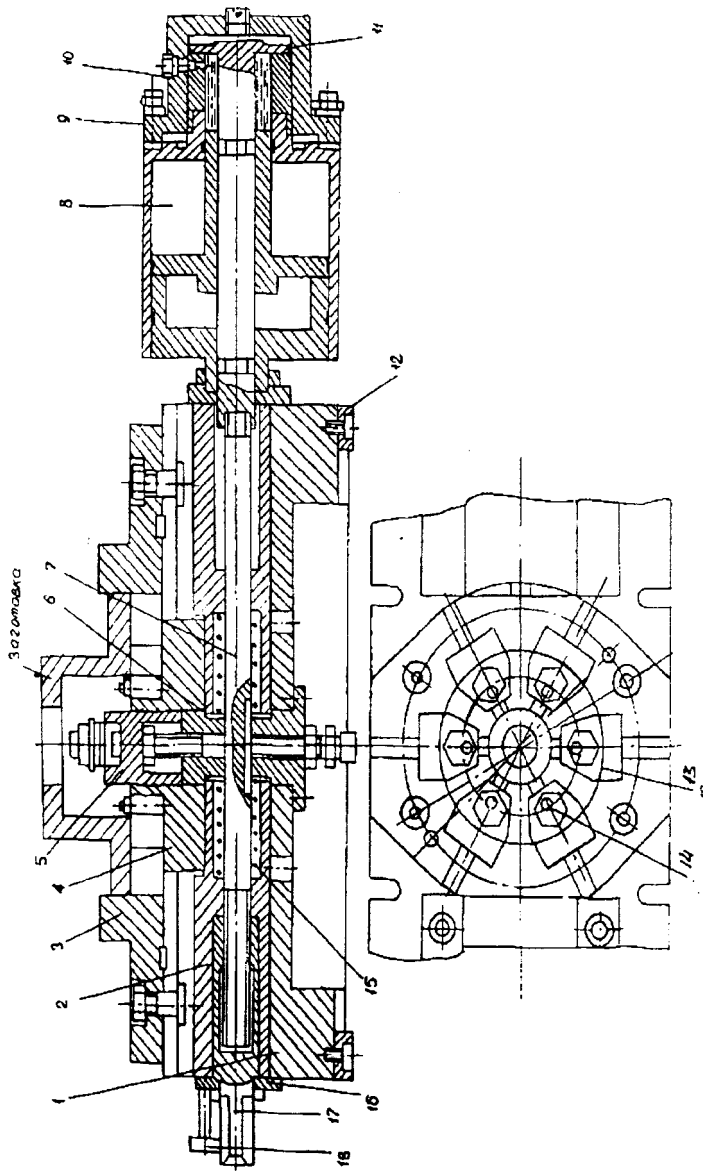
Переделываемое приспособление для сверления отверстий во фланцах стаканов и крышек
